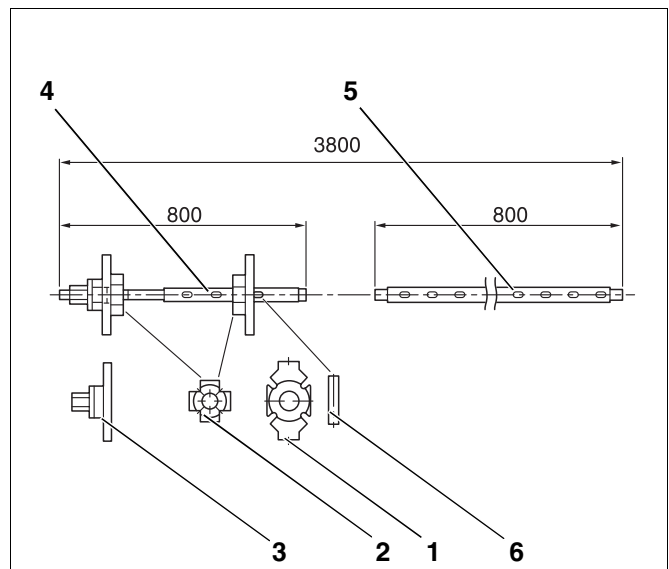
Kesselpresswerkzeug Größe 2.3 (Maße in mm)
